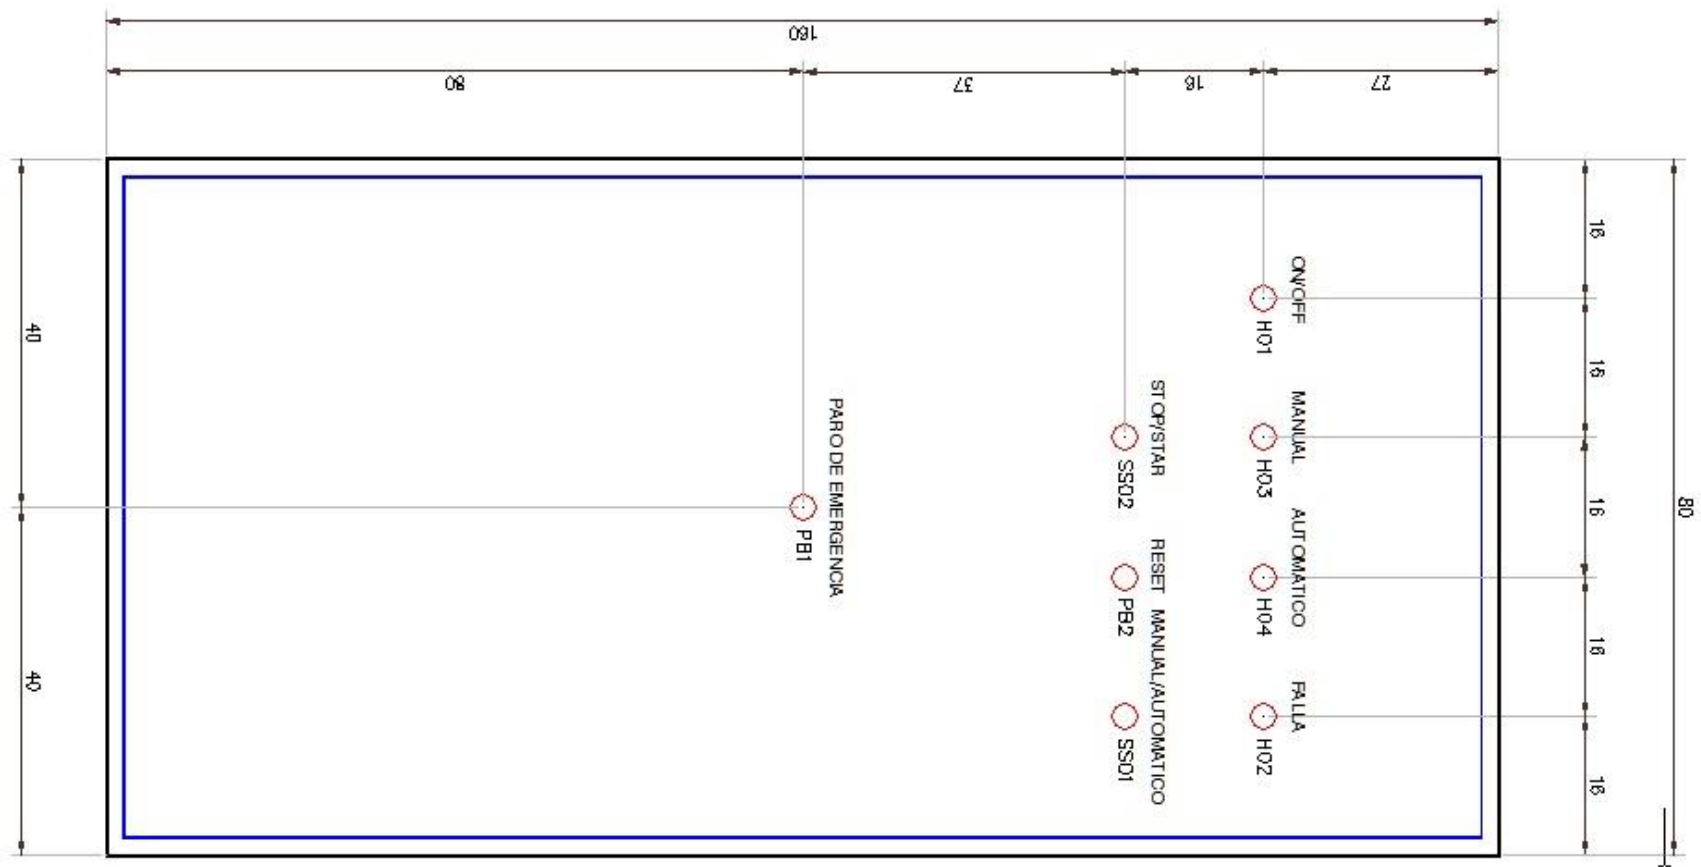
32: Diseño del tablero de control parte frontal.
